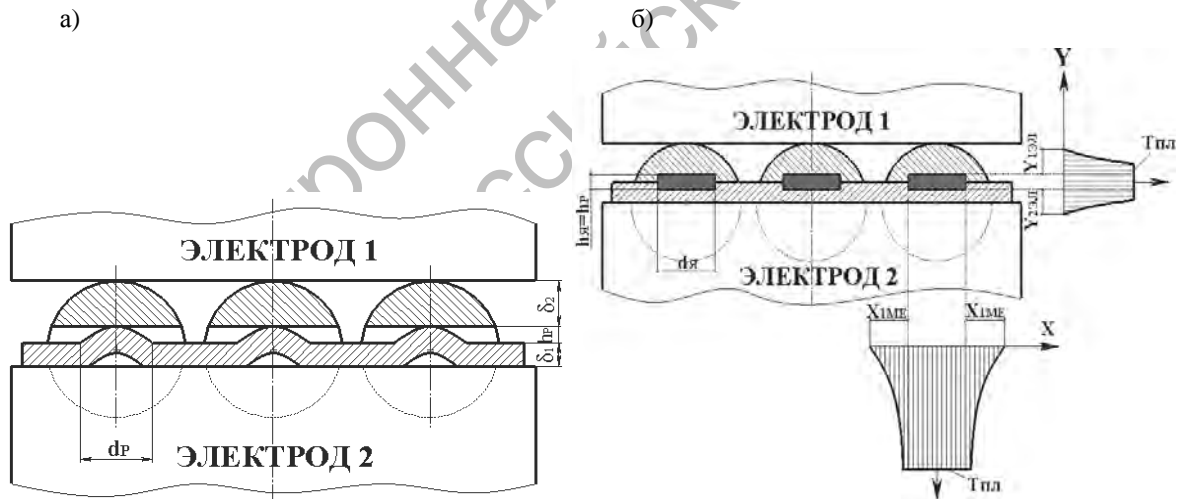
Расчетные схемы сварного соединения засова: а – геометрия деталей засова перед сваркой; б – схема расчета теплового баланса пакетного соединения деталей засова
